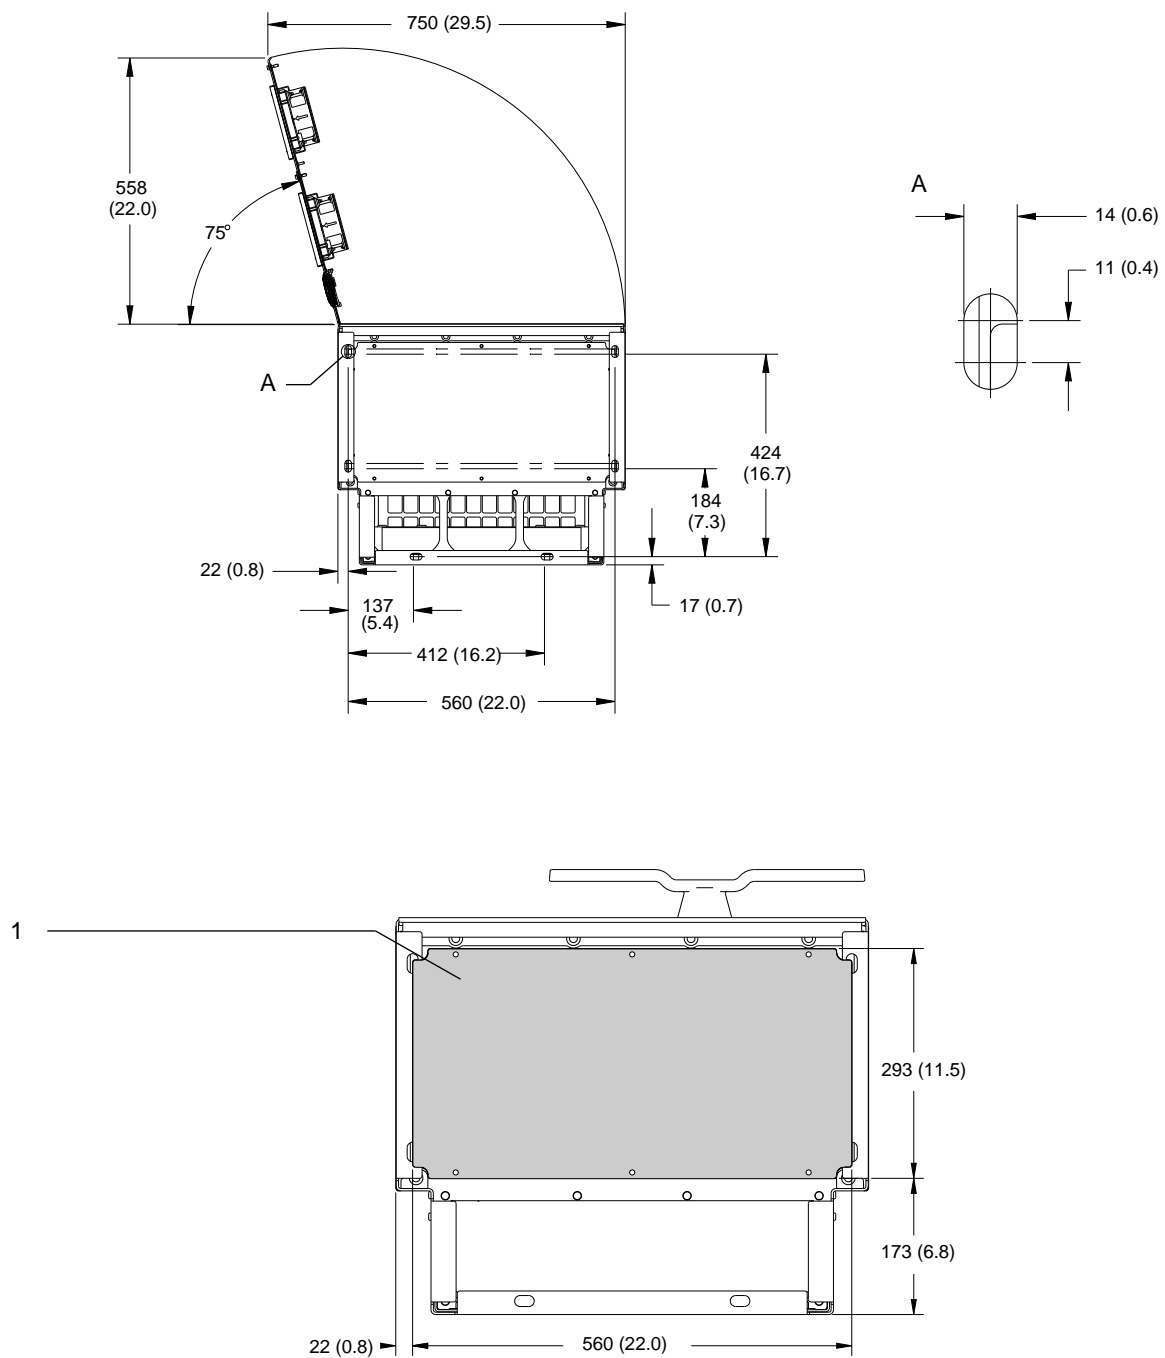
Espace pour la porte et dimensions de la plaque d'entrée des câbles pour E1h
